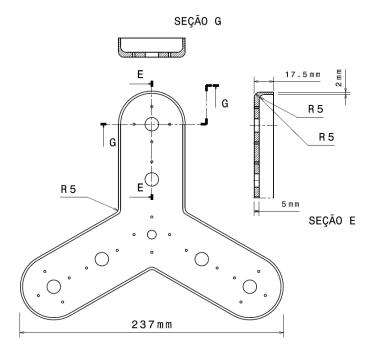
Detalhe de arredondamento nas paredes externa e interna.
